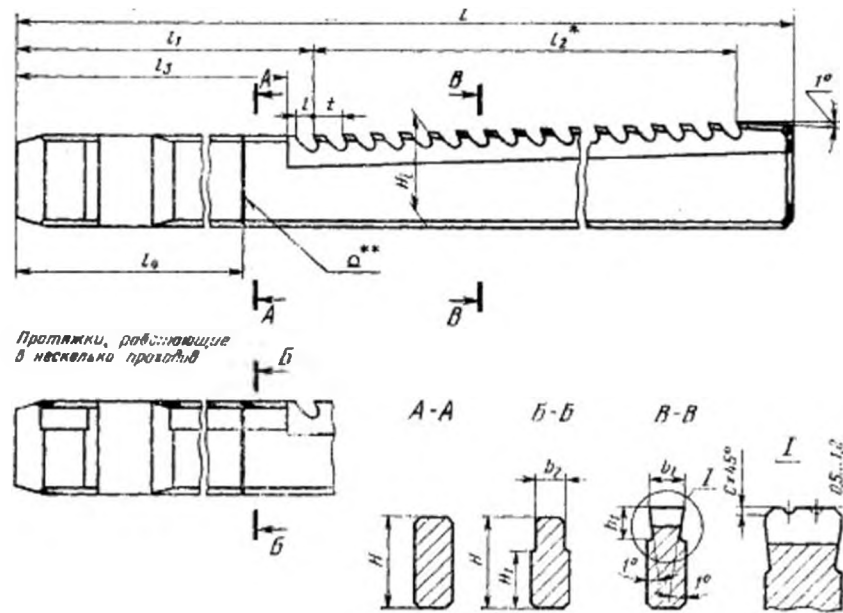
Шпонкова протяжка 2405-1052
